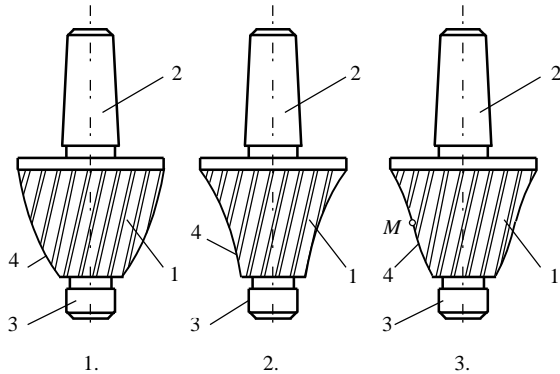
Инструменты для обработки сложных поверхностей деталей (а.с. №1271680).
